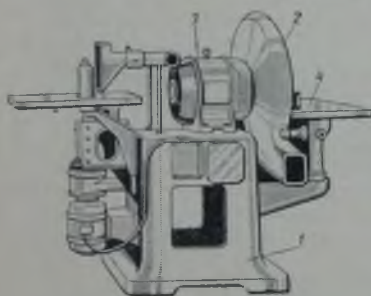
Шлифовальный станок, модель ШЛ-ДБ
